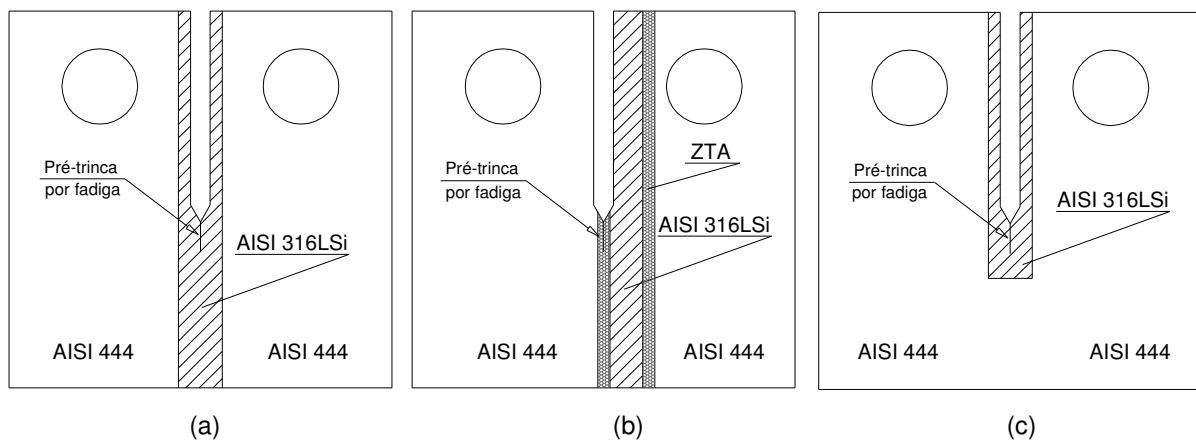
Representação esquemática das diferentes posições do entalhe em CPs do tipo tração-compacto, C(T), para ensaios sob carga constante; (a) pré-trinca na zona fundida; (b) pré-trinca na ZTA; (c) pré-trinca no cordão de solda parcial.
